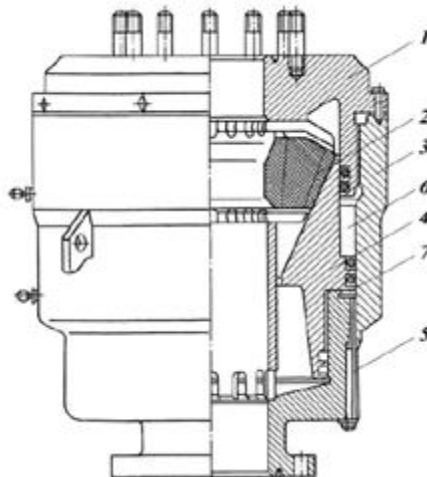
Универсальный превентор ПУГ 230х320: 1 – крышка, 2 – уплотнитель, 3 – корпус превентора, 4 – плунжер, 5 – трубки для подвода рабочей жидкости, 6 – верхняя запорная камера, 7 - нижняя запорная камера
